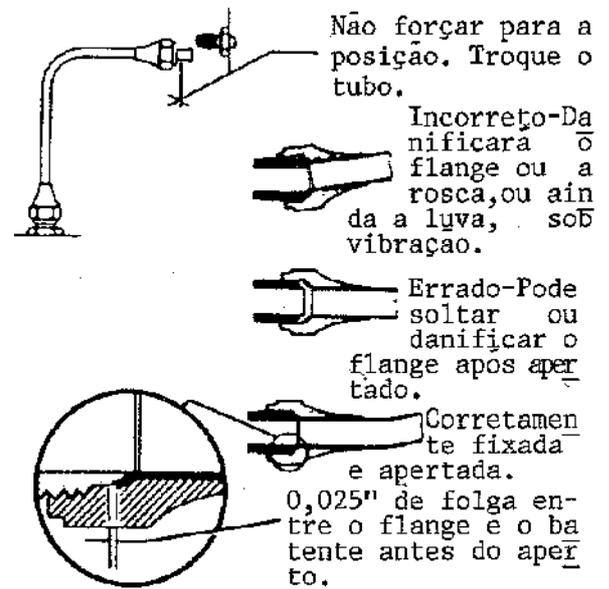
Métodos corretos e errados de instalar conexões flangeadas.
